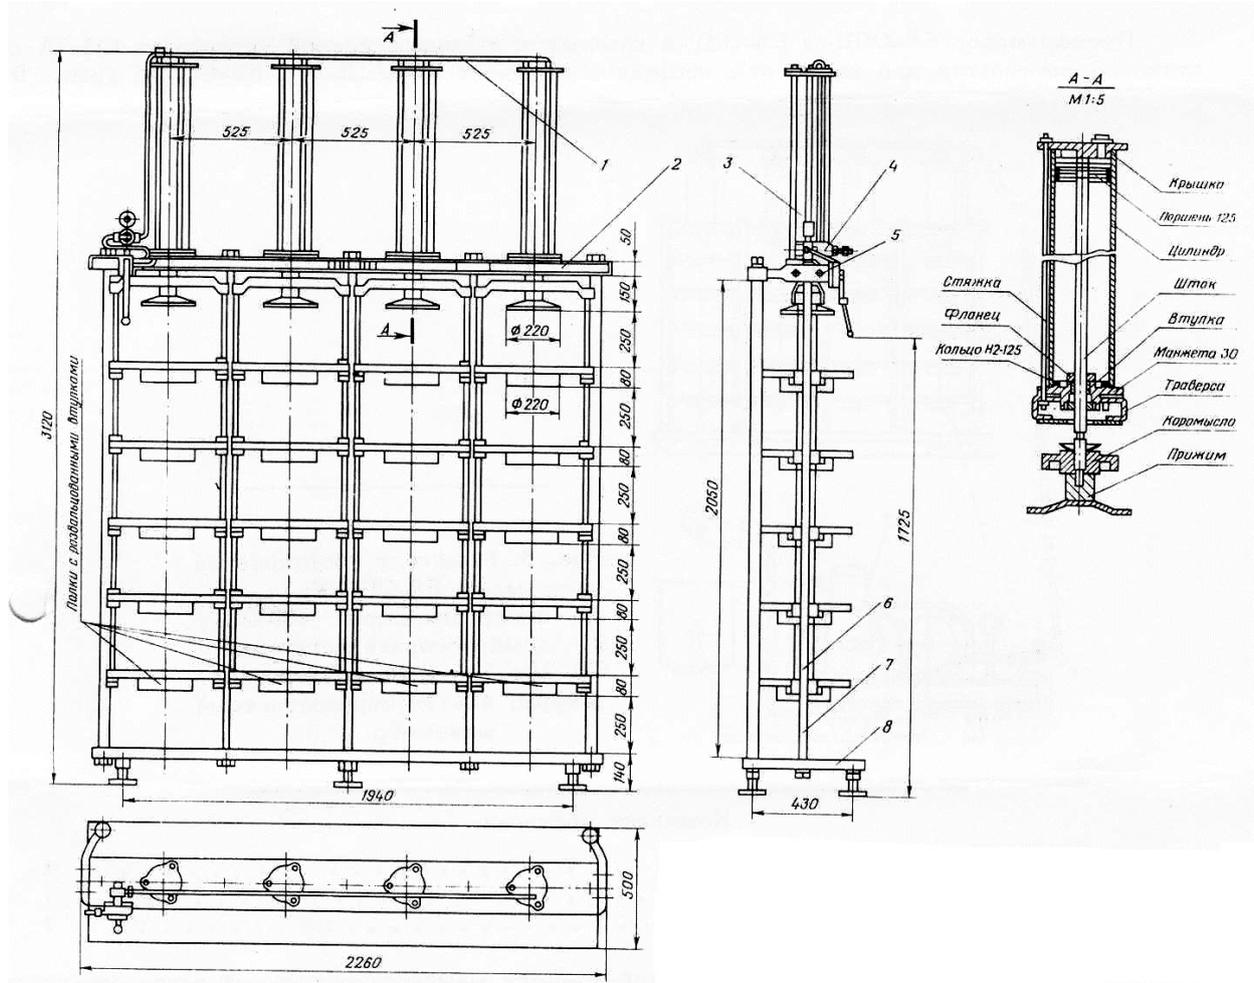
Общий вид пресса марки Е8-ОПГ: 1 – пневмосистема; 2 – траверса; 3 – пневмоцилиндр; 4 – кран управления; 5 – регулятор давления; 6 – прессующие полки; 7 – цилиндрическая стойка; 8 – основание
